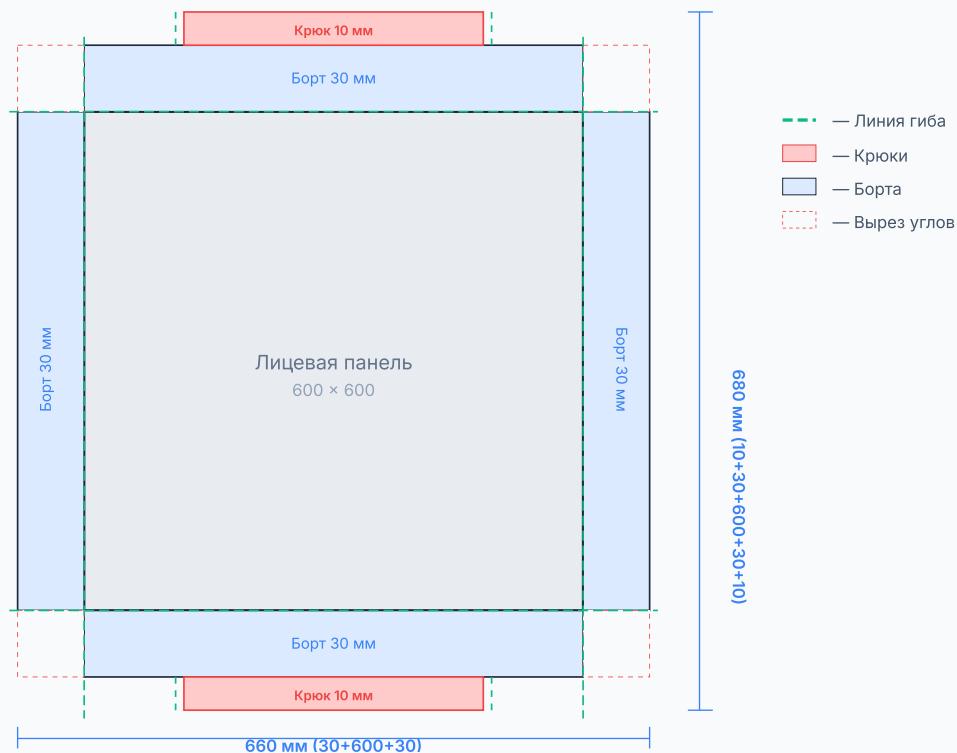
Развёртка кассеты Hook-On (заготовка догибки)
